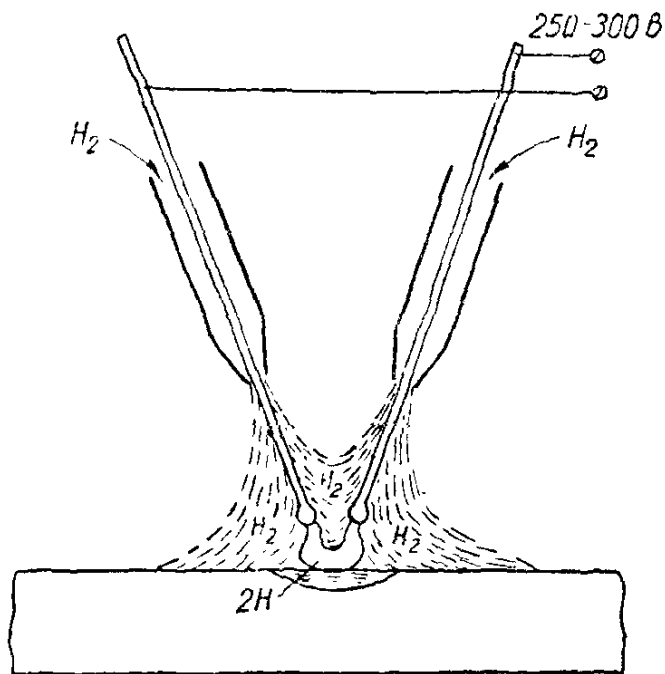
Дуговая сварка в защитном газе.
